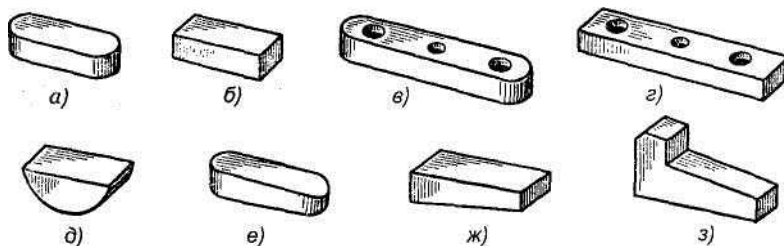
Конструкции шпонок: *а*, *в* — шпонки со скругленными торцами; *б*, *г* — шпонки с плоскими торцами;
